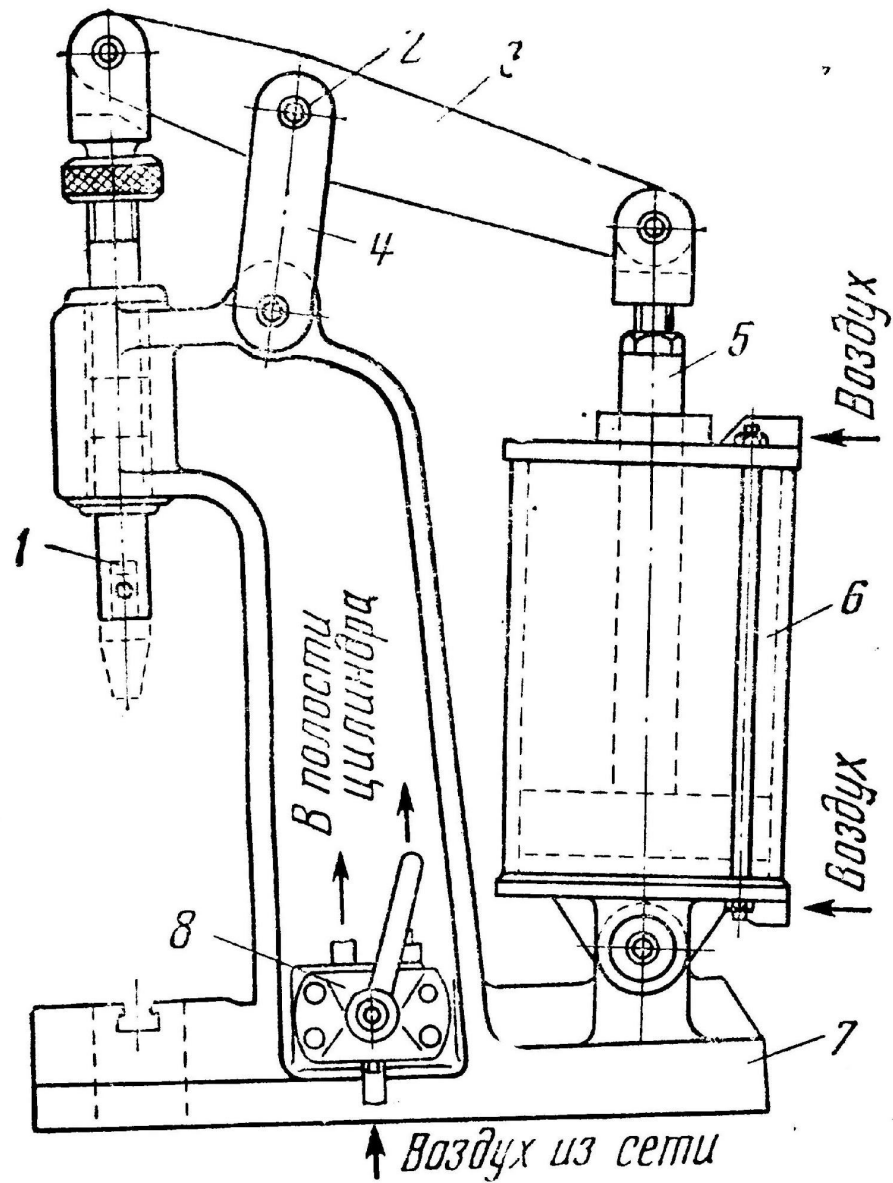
Гидравлический пресс для выпрессовки шкворней
